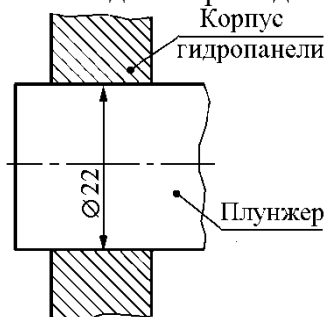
Схема соединения «плунжер-отверстие» в корпусе гидропанели
